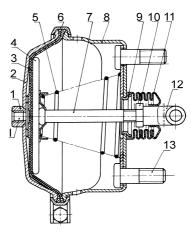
Тормозная камера1– бобышка; 2– крышка; 3- мембрана; 4– диск; 5 – пружина; 6–хомут; 7– шток; 8– корпус; 9–фланец; 10–гайка; 11– защитный чехол; 12– вилка; 13 - болт
